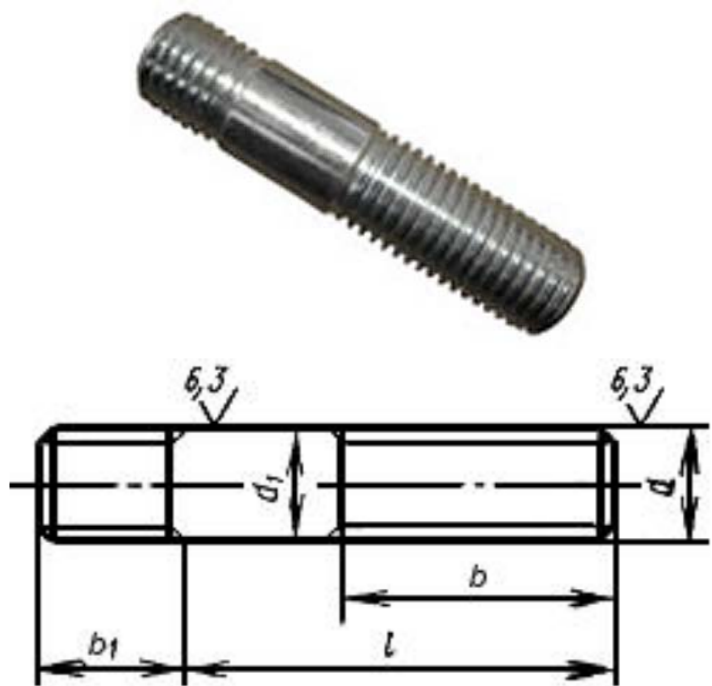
Шпилька для фланцевых соединений с ассиметричными резьбовыми концами (ГОСТ 22032)\
